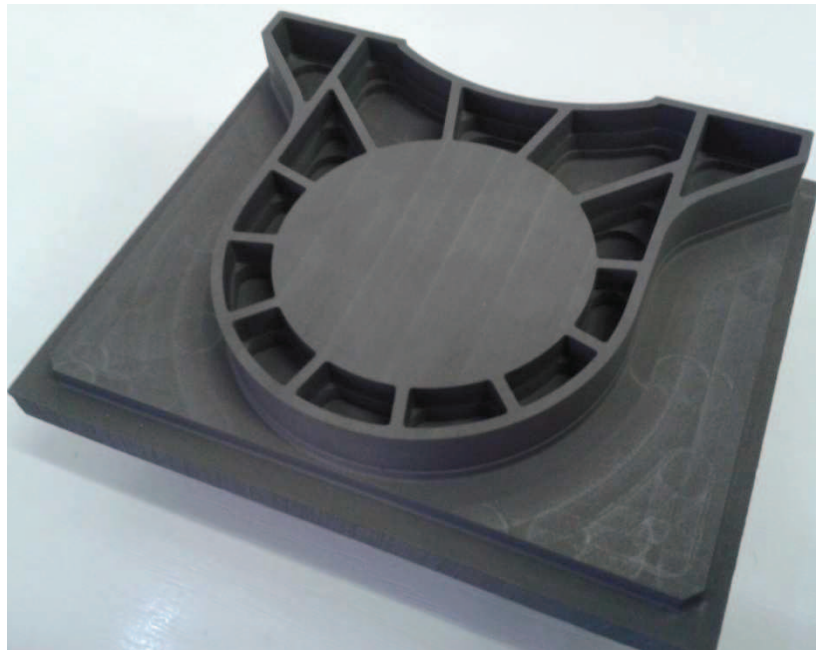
Nástroje pro frézování elektrody pro žebra.
